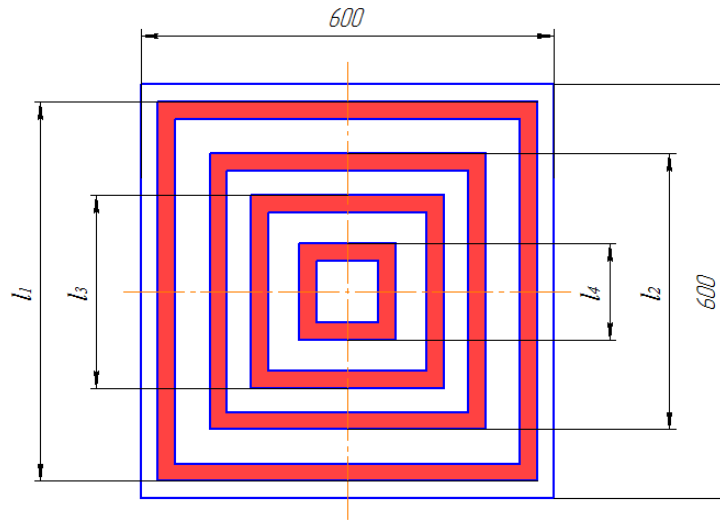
Конструкция нагревательной плиты с концентрическим расположением индукторов
